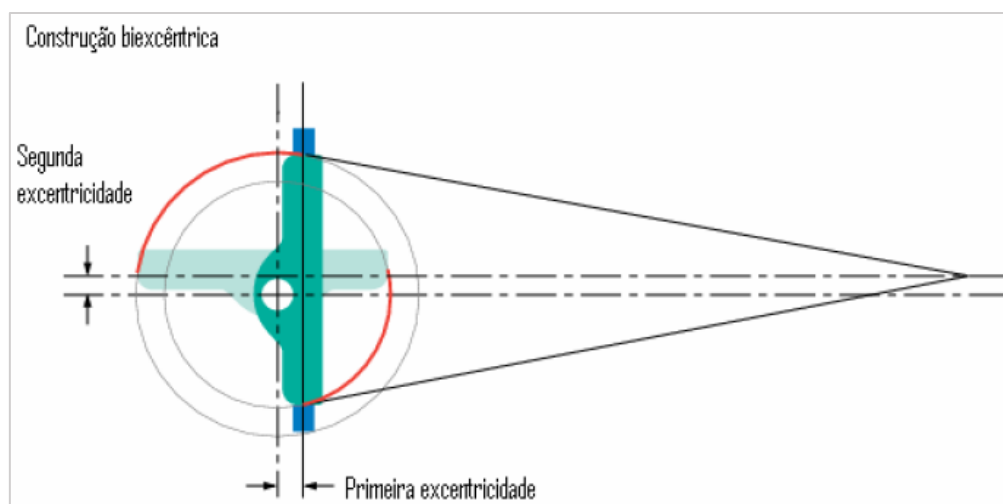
Disposição Geométrica da Vedação de Válvula Borboleta do tipo Bi-excêntrica
